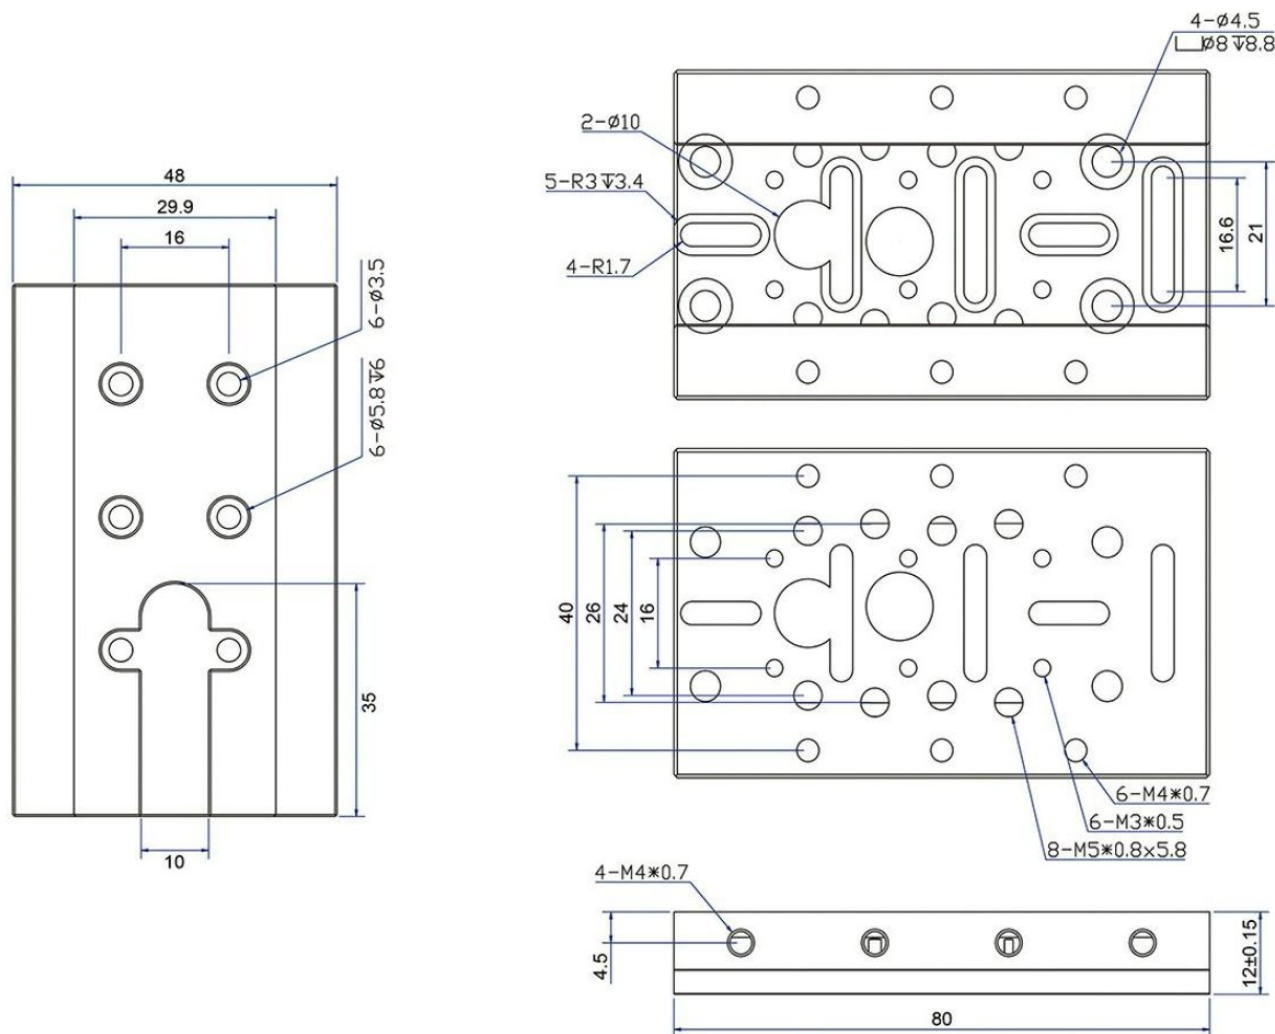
Габаритные и присоединительные размеры монтажной пластины.
